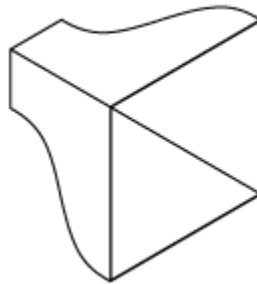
Armazón con tablero de plywood generando la cara interna Fuente: Generación Propia. SolidWorks(2018)
